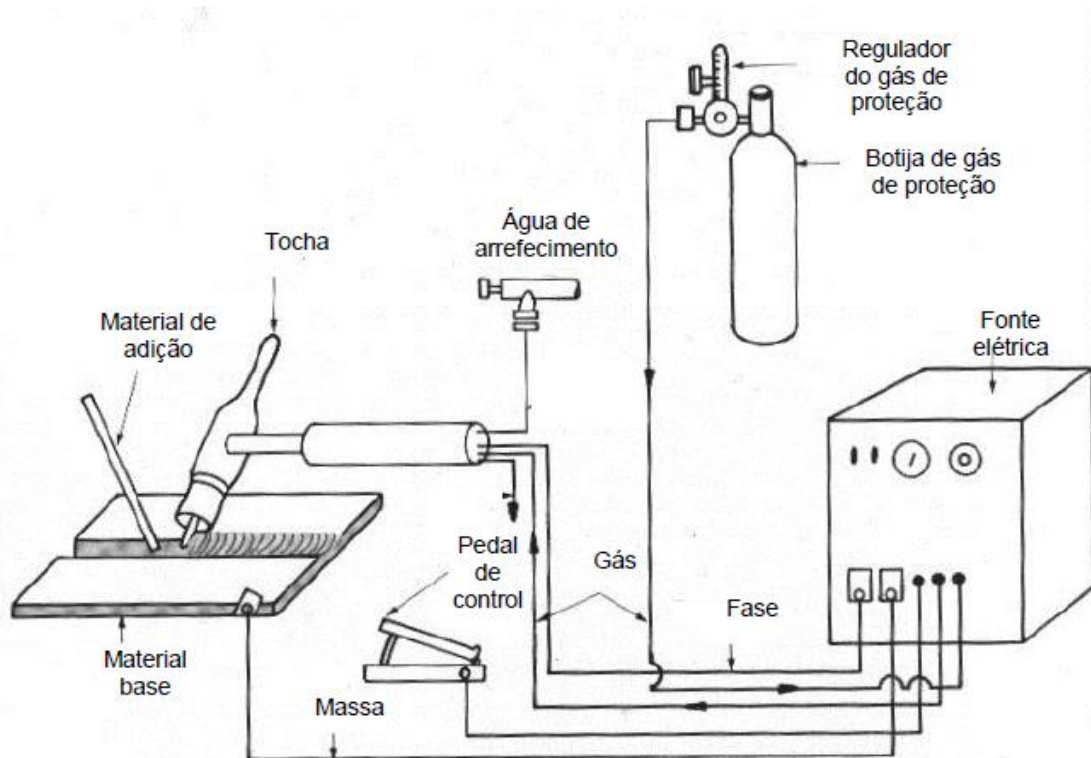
Esquema de máquina de soldar com processo TIG (adaptado de everlastgenerators).
